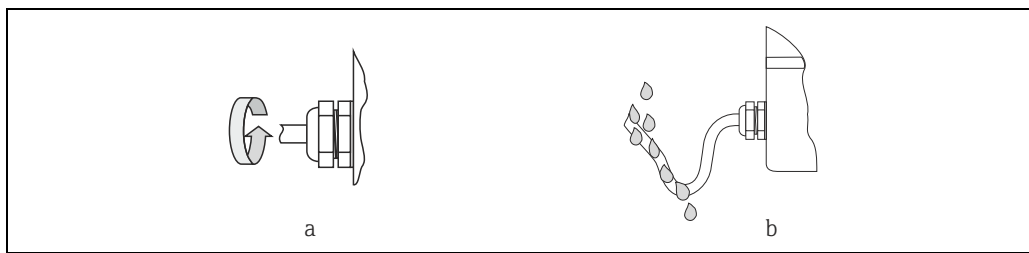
Instrucciones para la instalación, prensaestopas de entrada de cables
